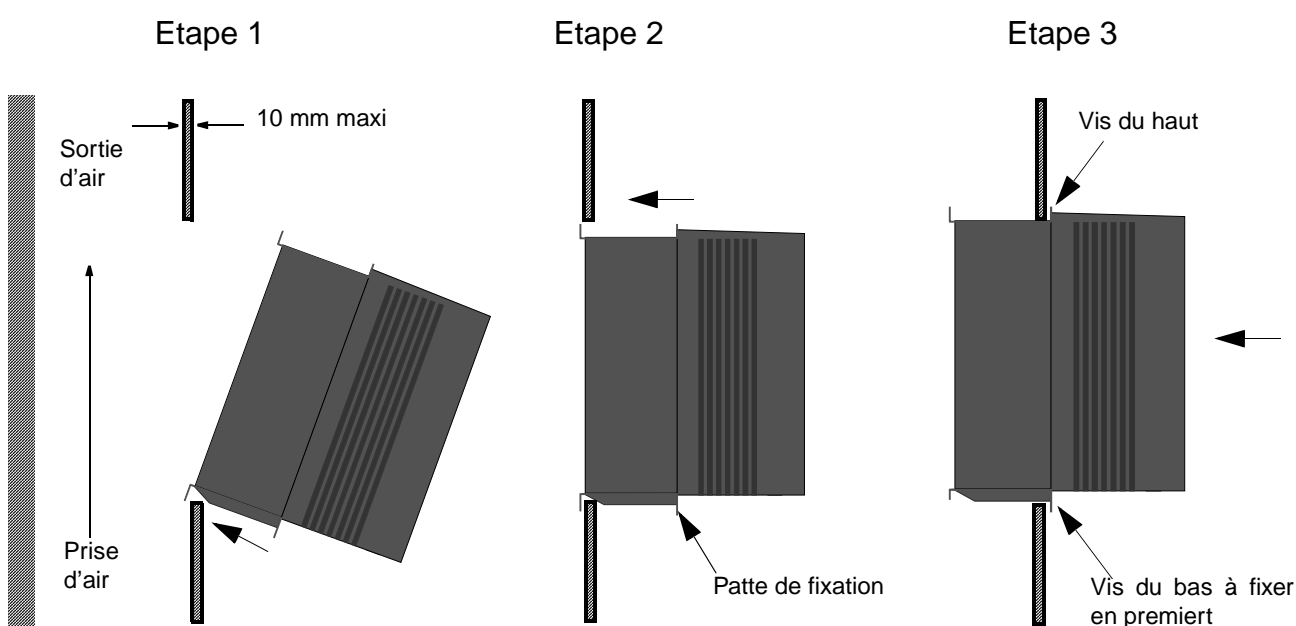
Montage de l'ACx 601 le long d'un conduit de ventilation.
